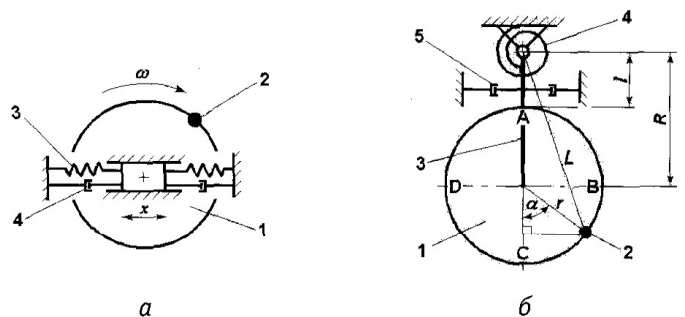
Спрощені схеми балансувальних верстатів з урахуванням тертя: а — зарезонансного (вид збоку); б — запропонованого (вид зверху)
